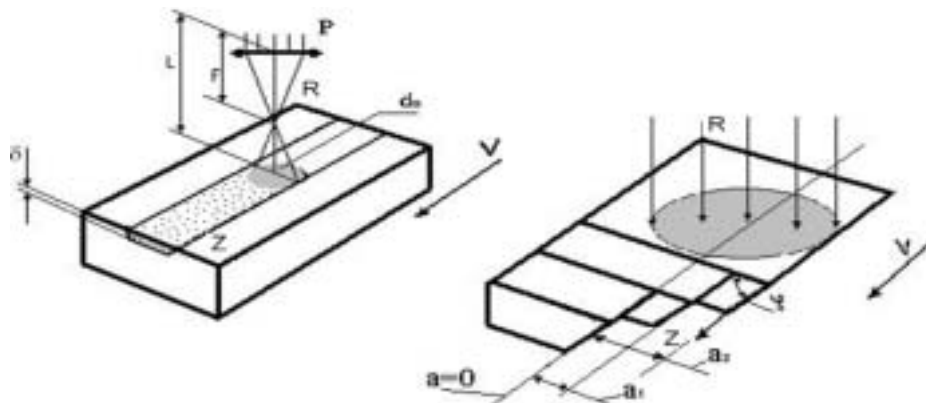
Схема лазерної обробки зразків призматичної та клиновидної форми
